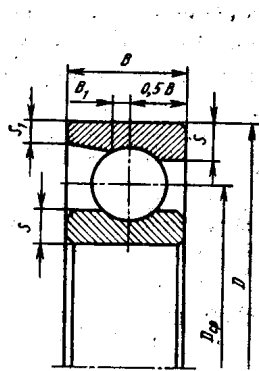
Подшипник шариковый радиально-упорный однорядный
